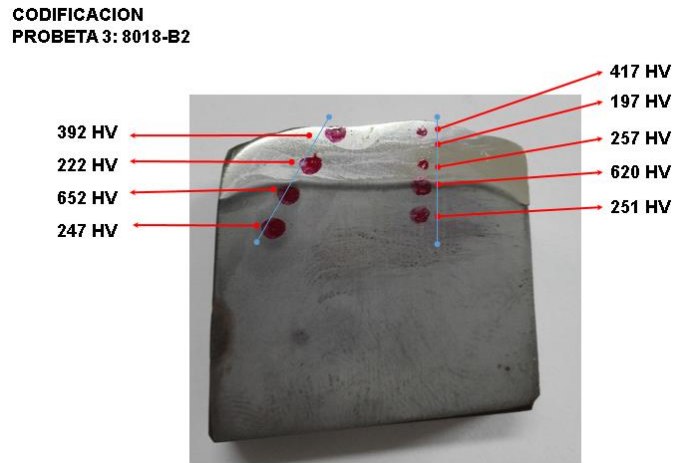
Probeta soldada con electrodo 8018-B2
